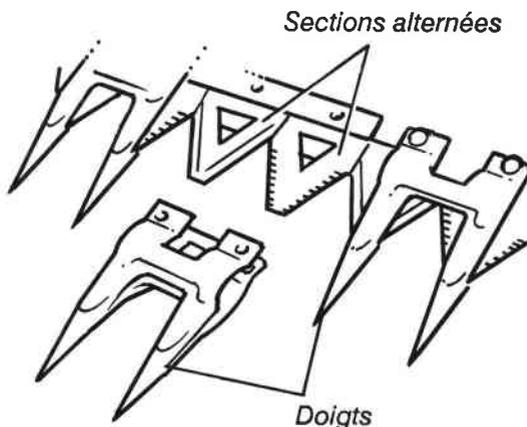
Vue partielle d'une barre de coupe à sections alternées.
